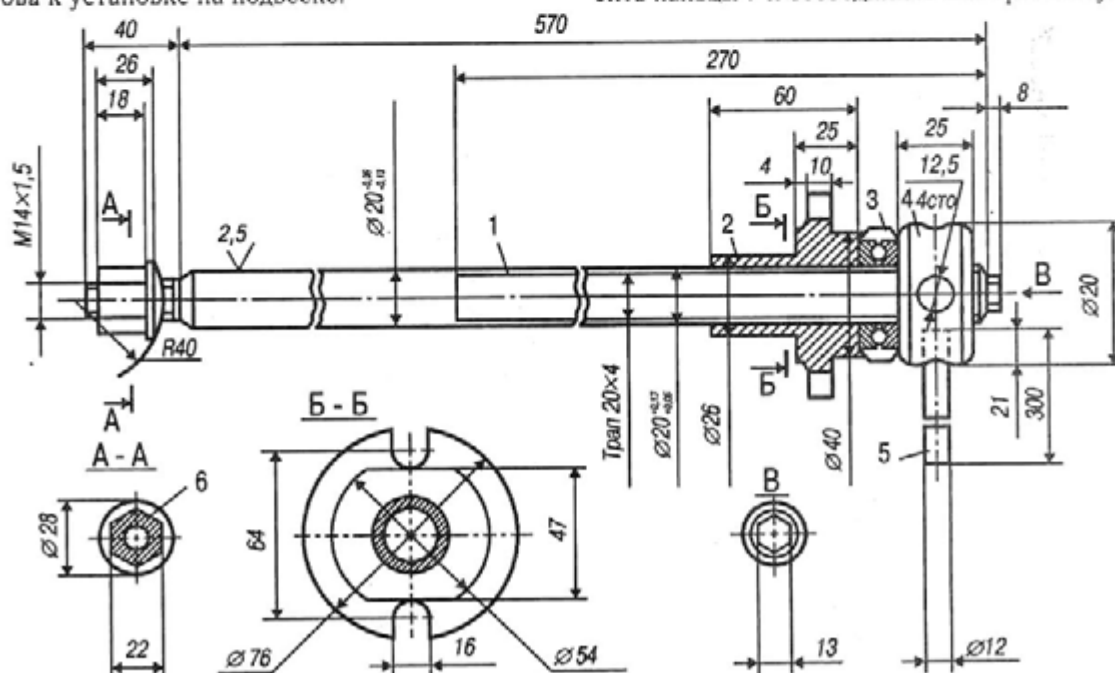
Приспособление для сжатия пружины передней подвески (7823-6703):
